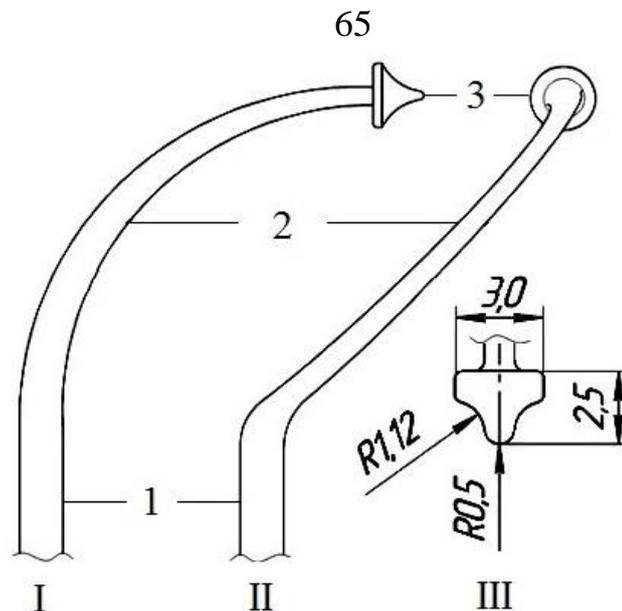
Схема разработанного нами штипфера: I - вид сбоку; II - вид сверху; III - параметры рабочей поверхности инструмента. 1 - ручка инструмента; 2 - изгиб рабочей части; 3 - рабочая поверхность
